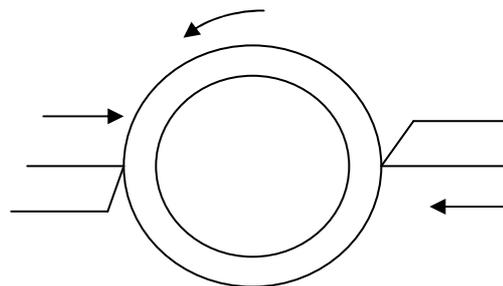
Отрезка заготовки на трубоотрезном станке
